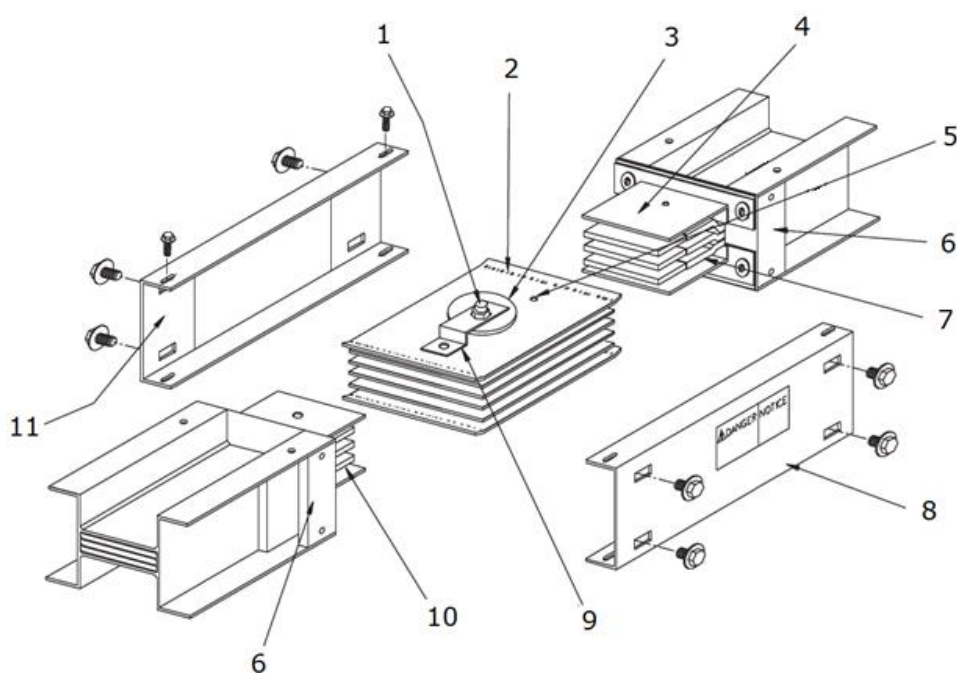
Схема соединения секций шинопровода внутренней установки: 1 – болт со срывной головкой; 2 – пресс-пластины стыковочного блока (верхняя и нижняя); 3 – шайба; 4 – пластина заземления; 5 – отверстие для фиксирующего болта; 6 – контактная пластина корпуса секции; 7 – изоляция шин; 8 – боковая крышка; 9 – фиксирующая пластина; 10 – шины; 11 – контактная пластина боковой крышки.
